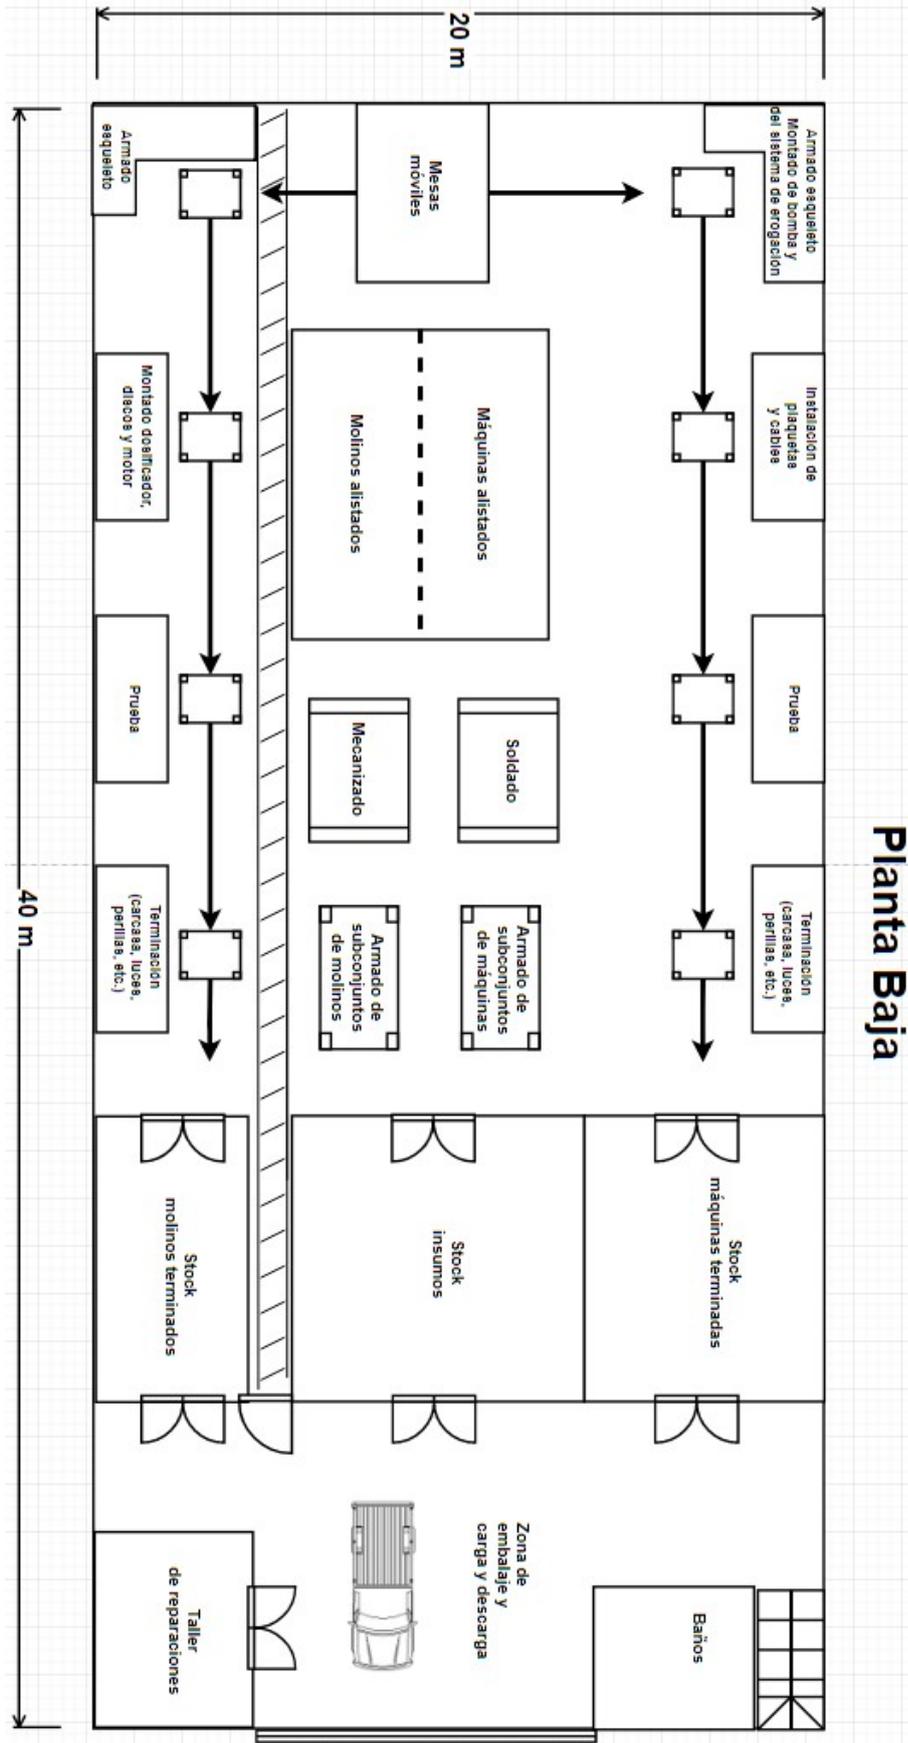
Lay Out de la planta baja de la nueva fábrica.
